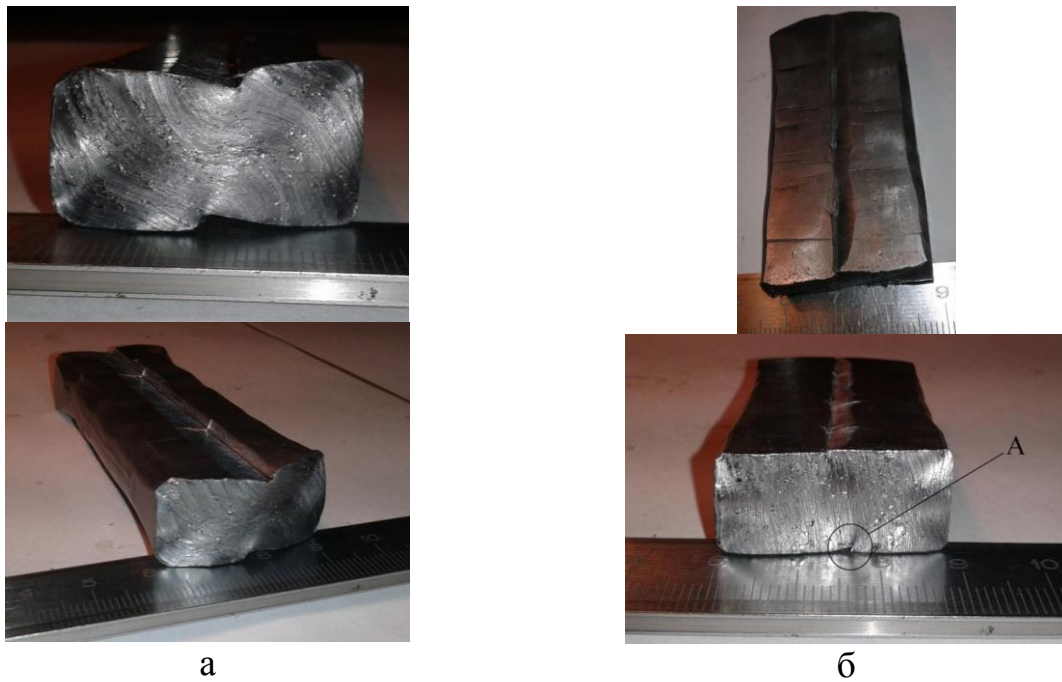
Заготовка для правки после протяжки ступенчатыми бойками: а – с углом скоса ступеньки 90° и б – правки плоскими бойками
